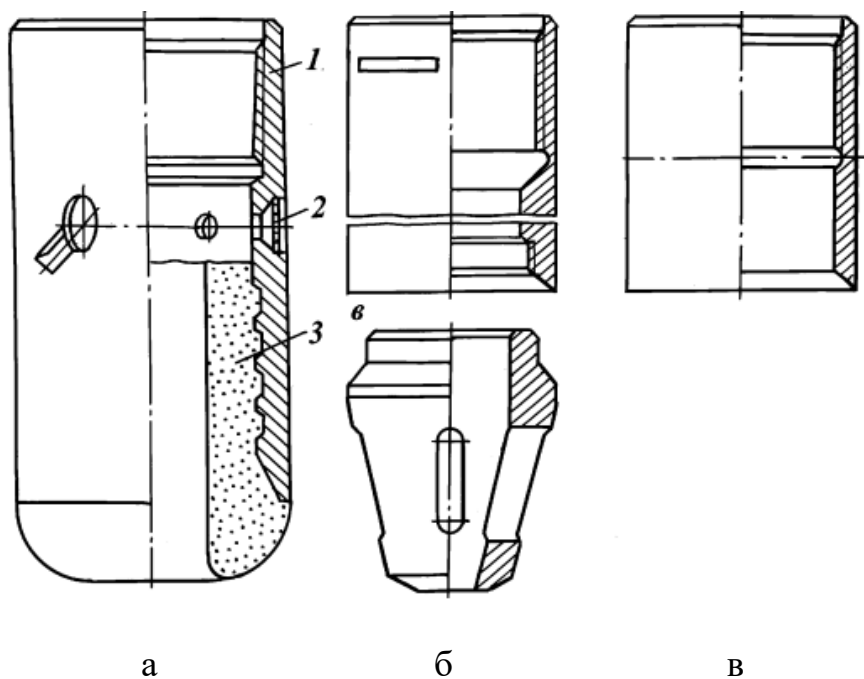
Башмаки колонные: а – типа БКМ: 1 – корпус; 2 – заглушка;
